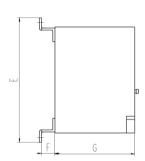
Габаритны и установочные размеры привода моторного МП-330Е
